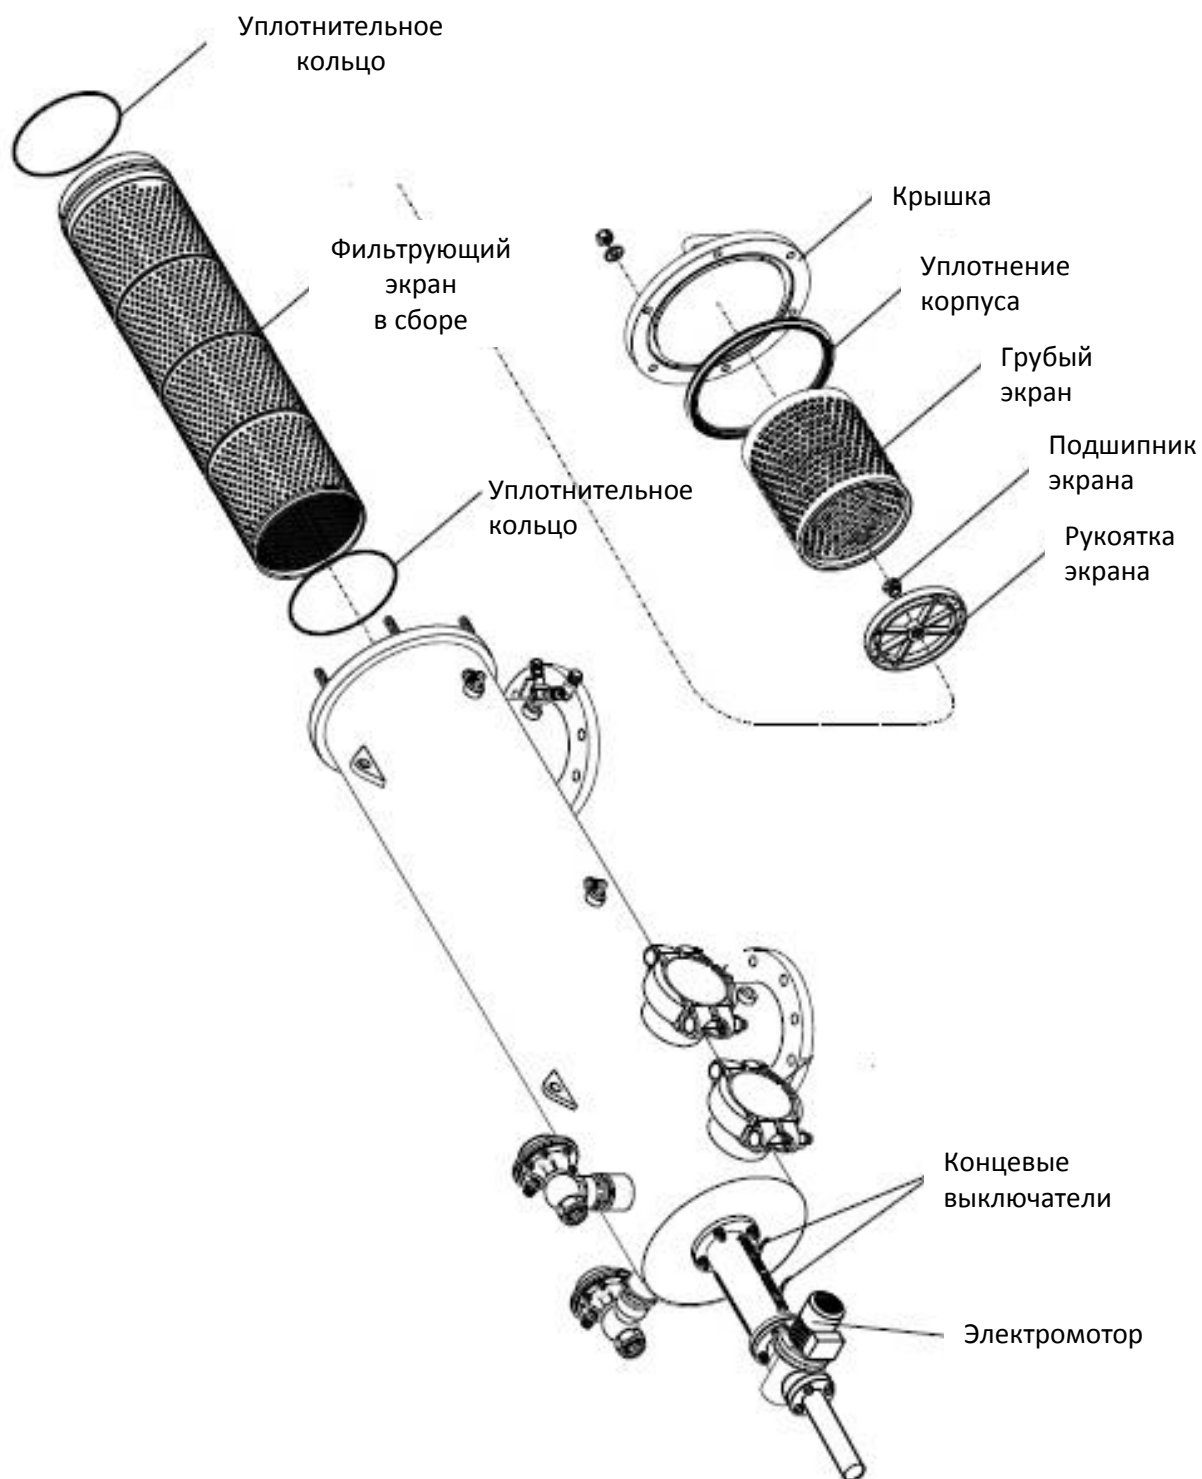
Демонтаж & Монтаж фильтрующего экрана
